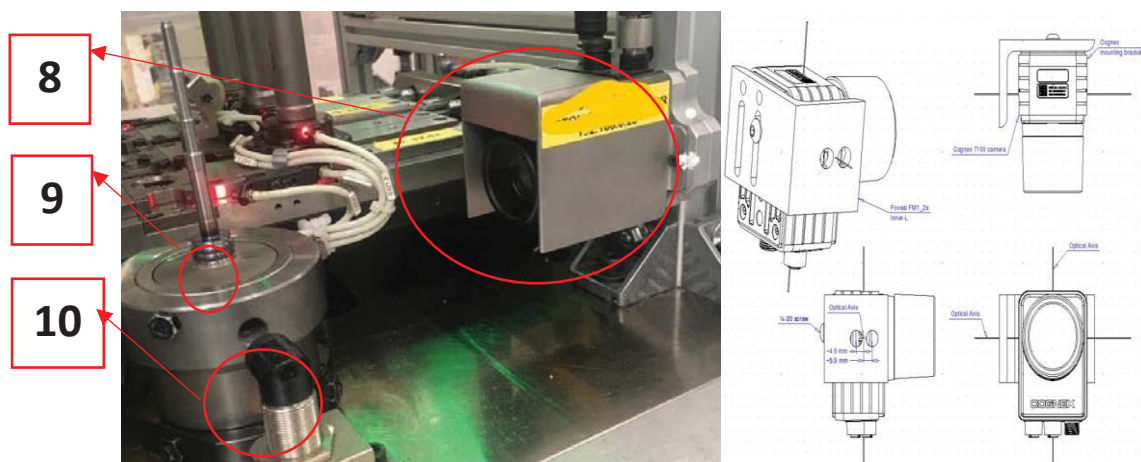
Detecție componente -senzor-cameră video (SWA-Shaft Wheel Assembly)
